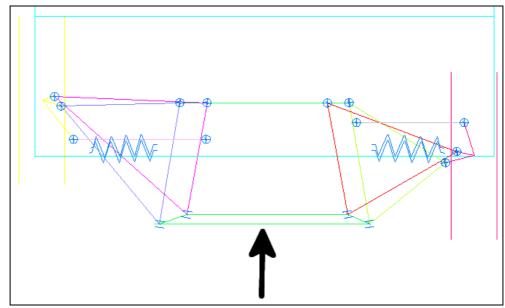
передняя подвеска, вид сверху (стрелкой показано направление движения автомобиля)
